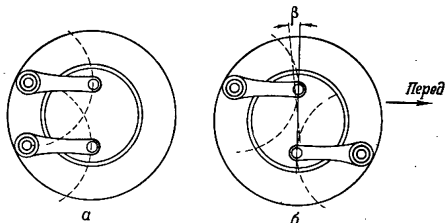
Схема подвески с двумя продольно расположенными рычагами
